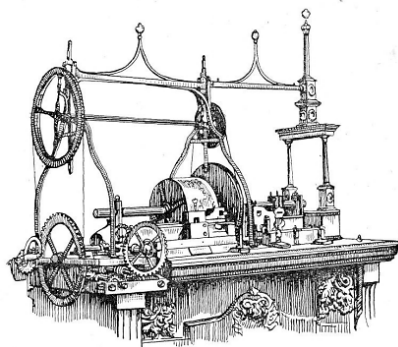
Токарно-копировальный станок Андрея Нартова³
